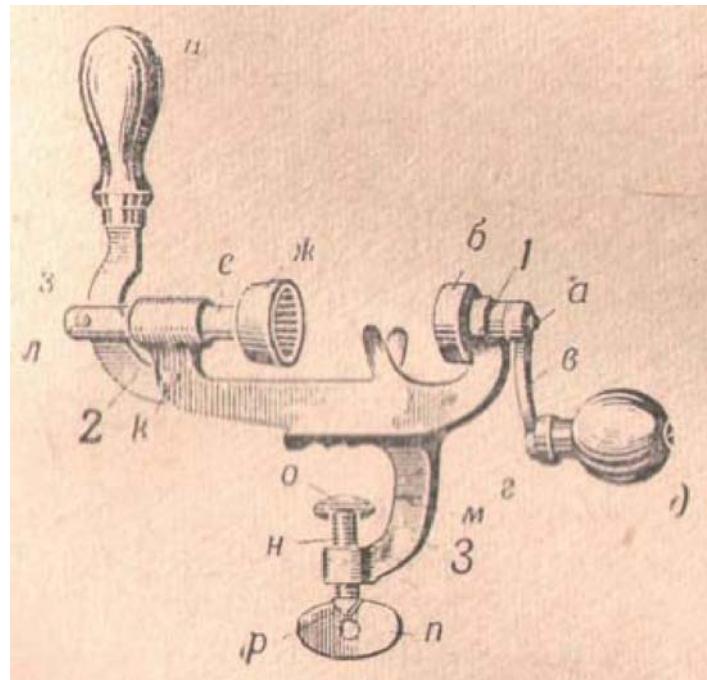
Закрутка настольная: 1 - узел матрицы: а - шпиндель матрицы, б - матрица, в- рычаг рукоятки, г- ось рукоятки, д - рукоятка; 2 - узел прижимного приспособления: е - шпиндель, ж - прижимная шайба, з - серповидный рычаг, и - рукоятка серповидного рычага, к - шарнирная ось, л - штилька; 3 - узел, крепящий закрутку к столу; м-кронштейн, н - винт, о - прижимная шайба, п - барашек винта, р - коническая штилька
